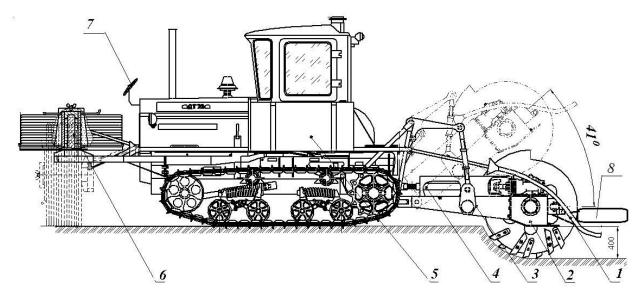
Агрегат для прокладки шланговых зарядов взрывчатых веществ. 1— шлангоукладчик, 2 — редуктор с фрезой, 3 —рама орудия, 4 — кардан, 5 — трактор ДТ-75 МХ, 6 — гидроуправляемая шланговая катушка, 7 — зеркало обзора катушки, 8 — засыпатель щели.
